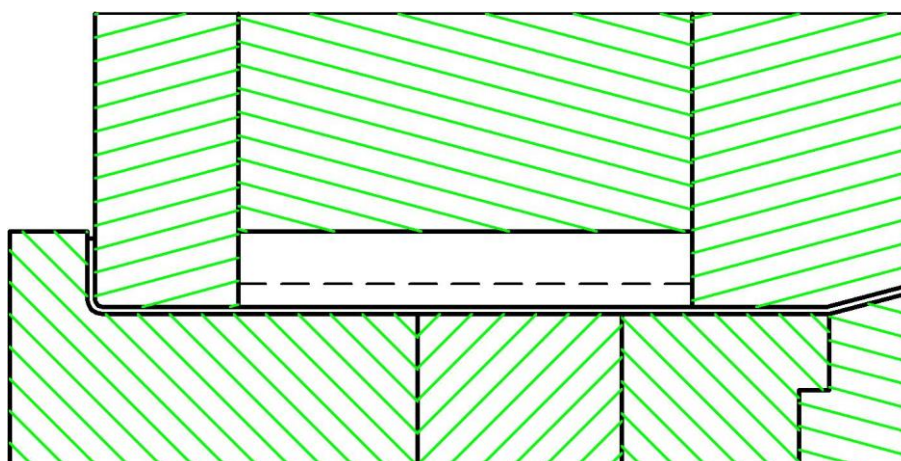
Гибка заготовки до окончательного изделия (вид сбоку)
